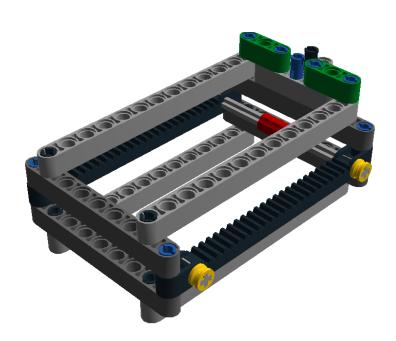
Конструкция с реечной передачей, для перемещения захвата вглубь ячейки
